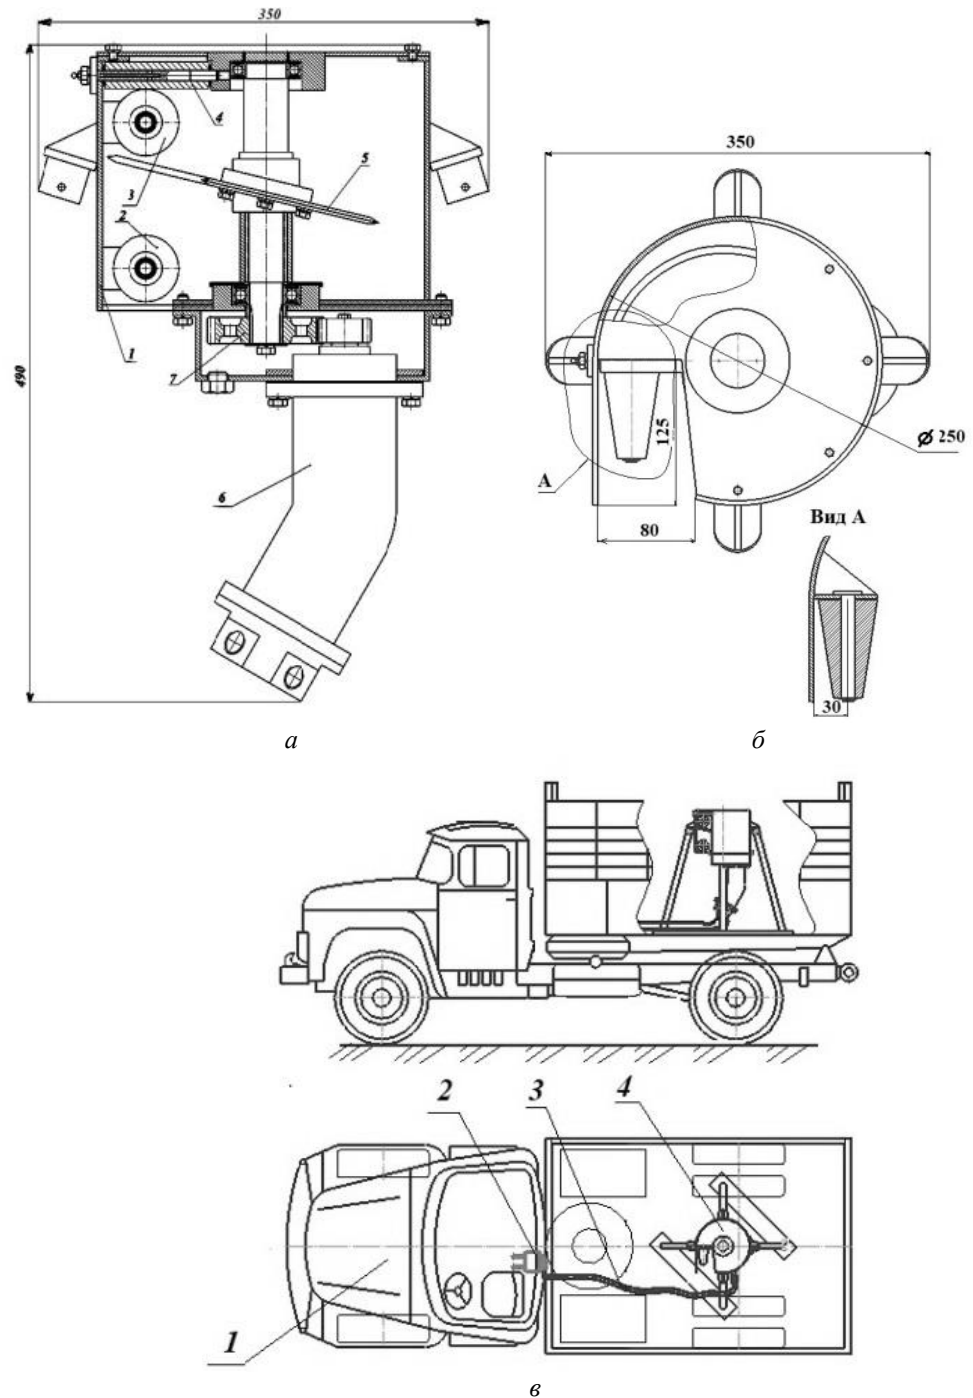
Чертеж рабочего органа измельчителя веток: *а* – вид сбоку (*1* – корпус, *2, 3* – ролики конические, *4* – ролик цилиндрический, *5* – нож, *6* – гидродвигатель, *7* – редуктор); *б* – вид сверху; *в* – общий вид установки на автомобиле (*1* – автомобиль, *2* – гидрораспределитель, *3* – шланги, *4* – измельчитель)
